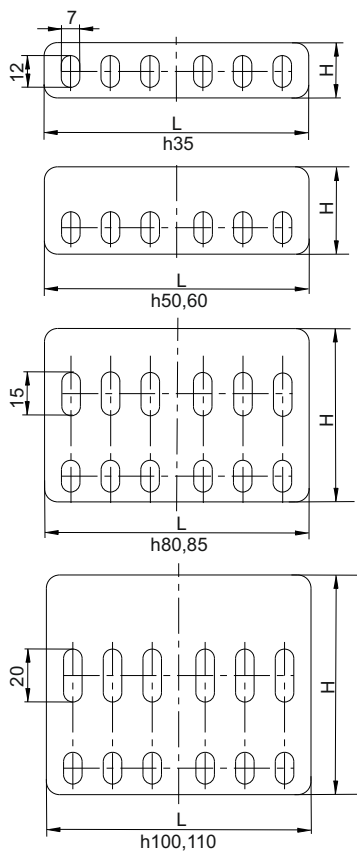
Пластина соединительная / Figure 1 – Connecting plate
